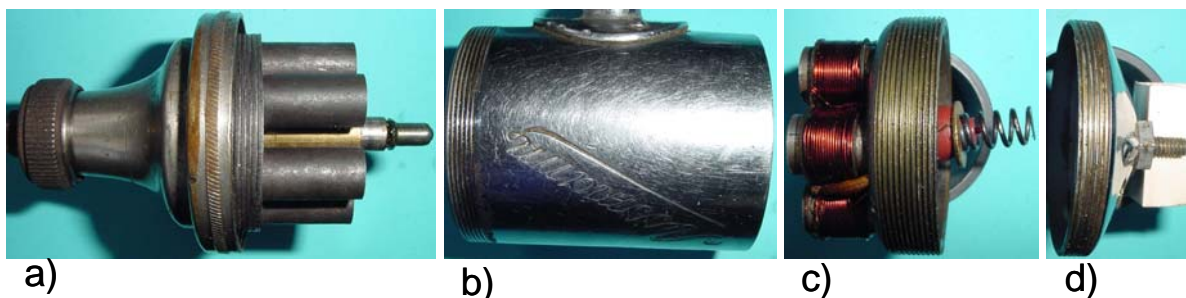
Baugruppen: a) Lagerhals mit Erregersystem, b) Gehäusemantel, c) Anker mit der Kontaktfeder d) Boden
